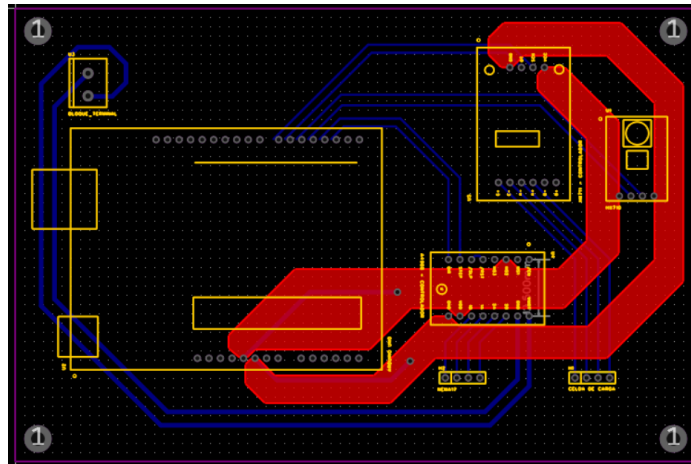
Disposición de componentes en la PCB de la plataforma de pruebas
